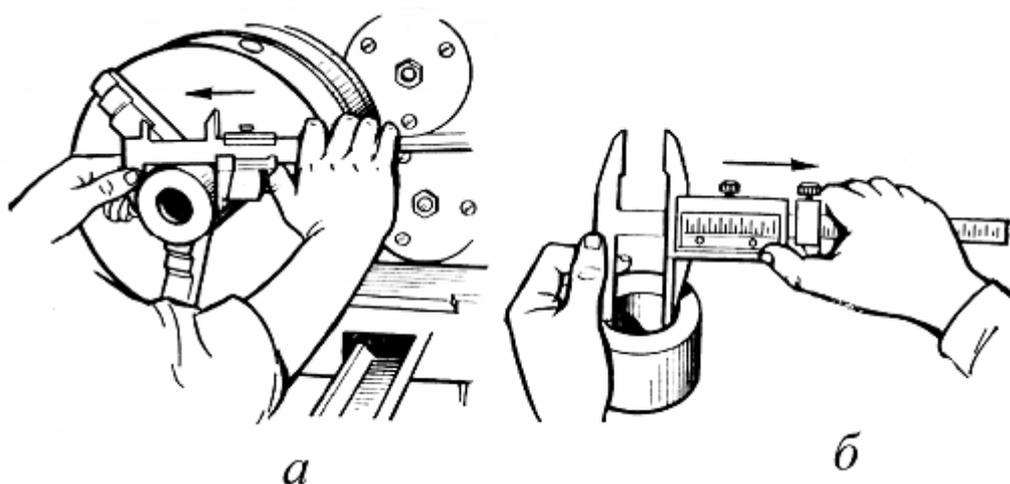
Измерение штангенциркулем наружных (а) и внутренних (б) размеров закрепленной детали
